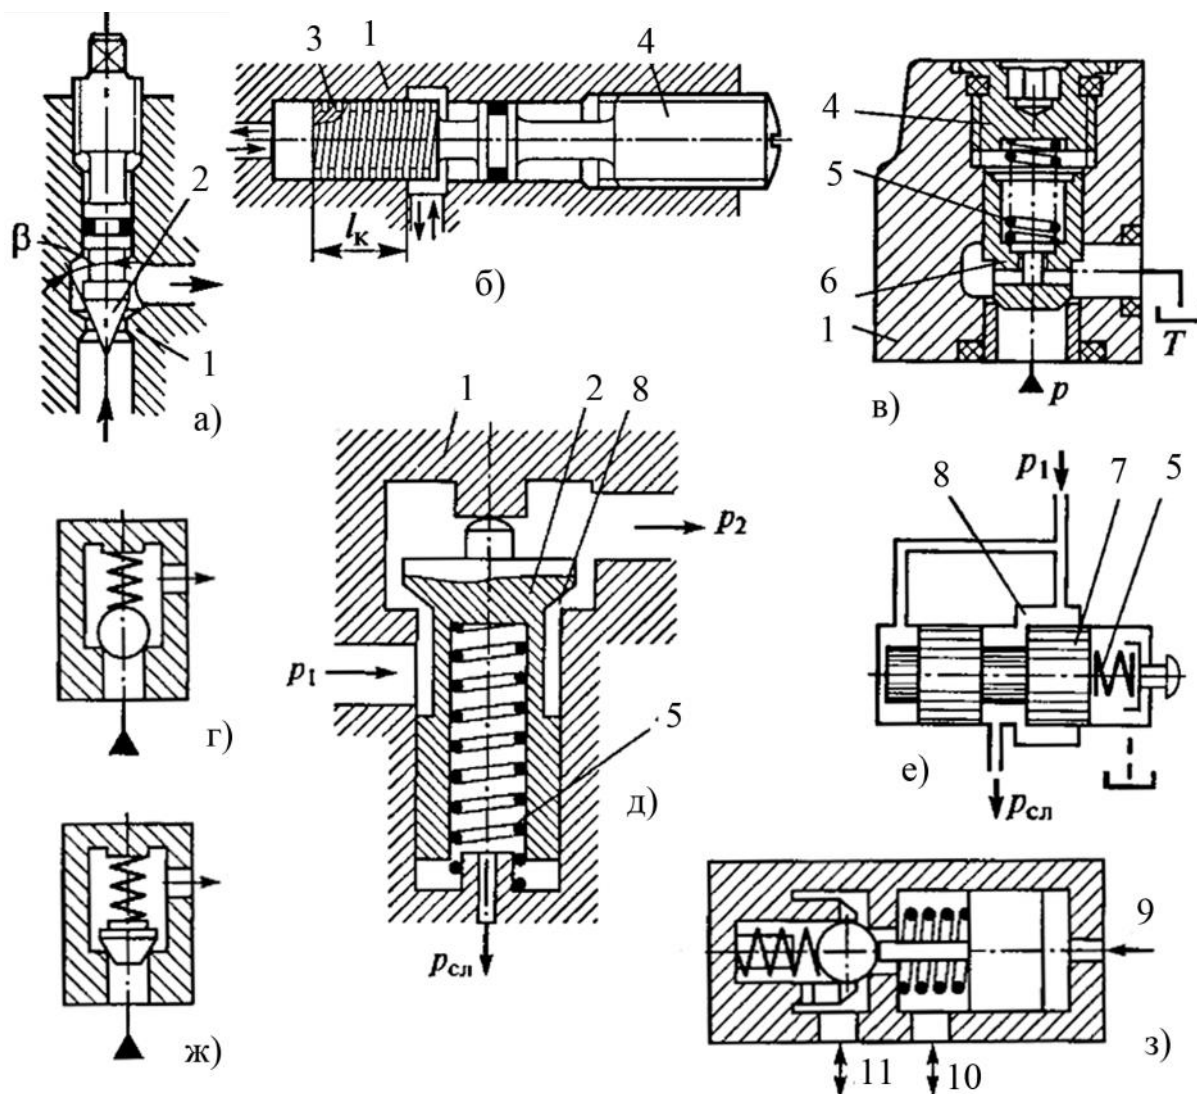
Конструкция основных элементов гидроаппаратуры: 1 – корпус; 2, 6 – запорно-регулирующий элемент; 3 – плунжер; 4 – регулировочный винт; 5 – пружина; 7 – золотник; 8 – щель; 9 – гидролиния управления; 10, 11 – гидролинии подвода и отвода РЖ; а – игольчатый регулируемый гидродроссель; б – линейный регулируемый гидродроссель; в – предохранительный клапан прямого действия; г – обратный шариковый; д – редукционный клапан прямого действия; е – переливной клапан прямого действия; ж – обратный конусный; з – односторонний гидрозамок
